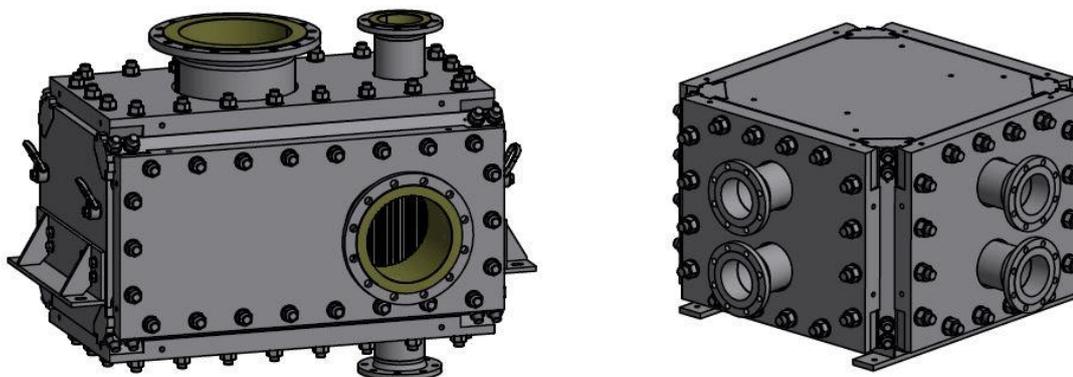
Аппарат теплообменный пластинчатый сварной типа SB горизонтального исполнения (слева) и вертикального исполнения (справа)
